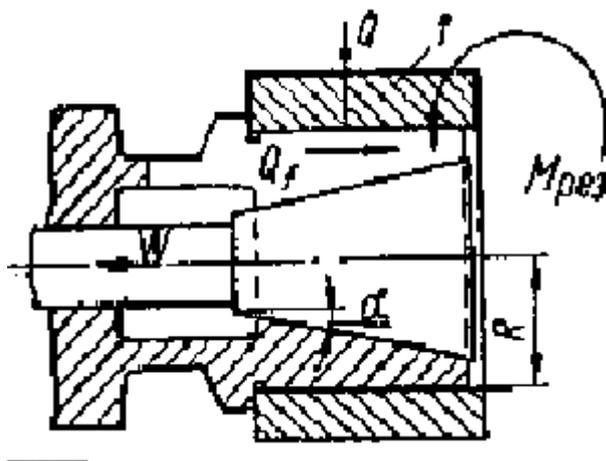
Схема действующих сил при закреплении заготовки в разжимной оправке
